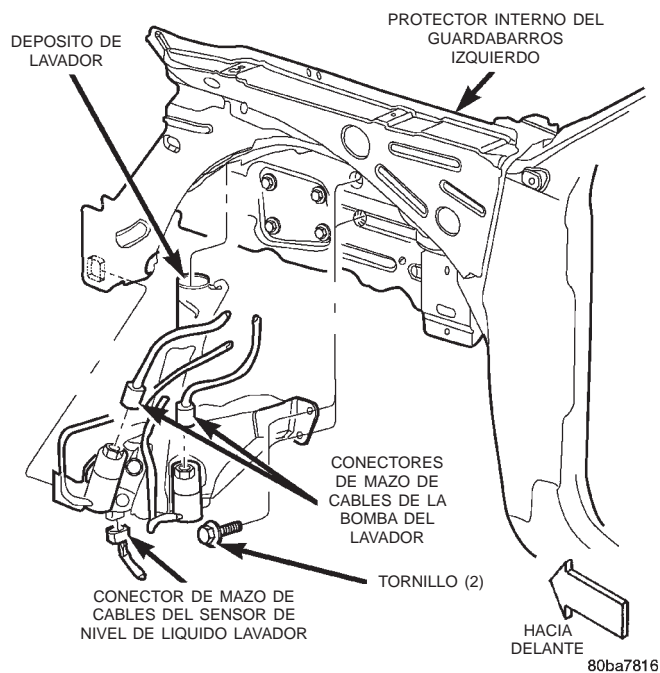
Desmontaje e instalación del depósito de líquido lavador
